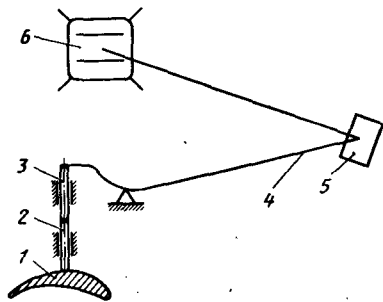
Схема опико-механического прибора ПОМКЛ-4 для контроля профиля пера лопаток компрессора:
